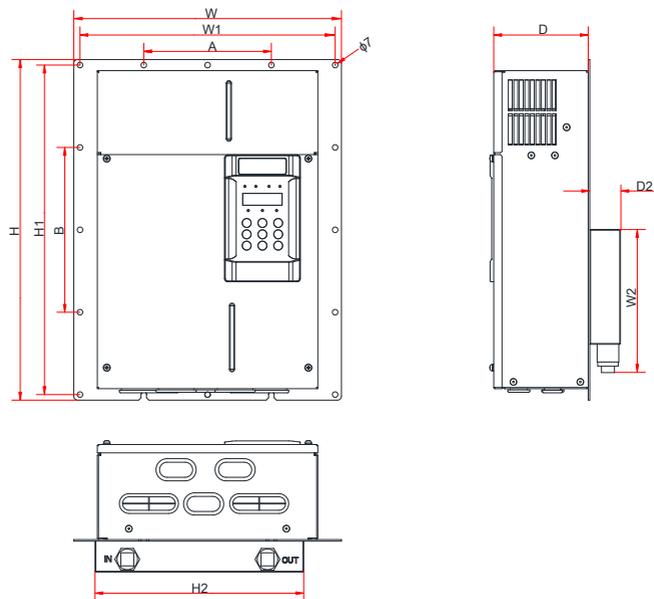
IS580T035R1-H~IS580T70-R1-H 外型尺寸及安装尺寸示意图
